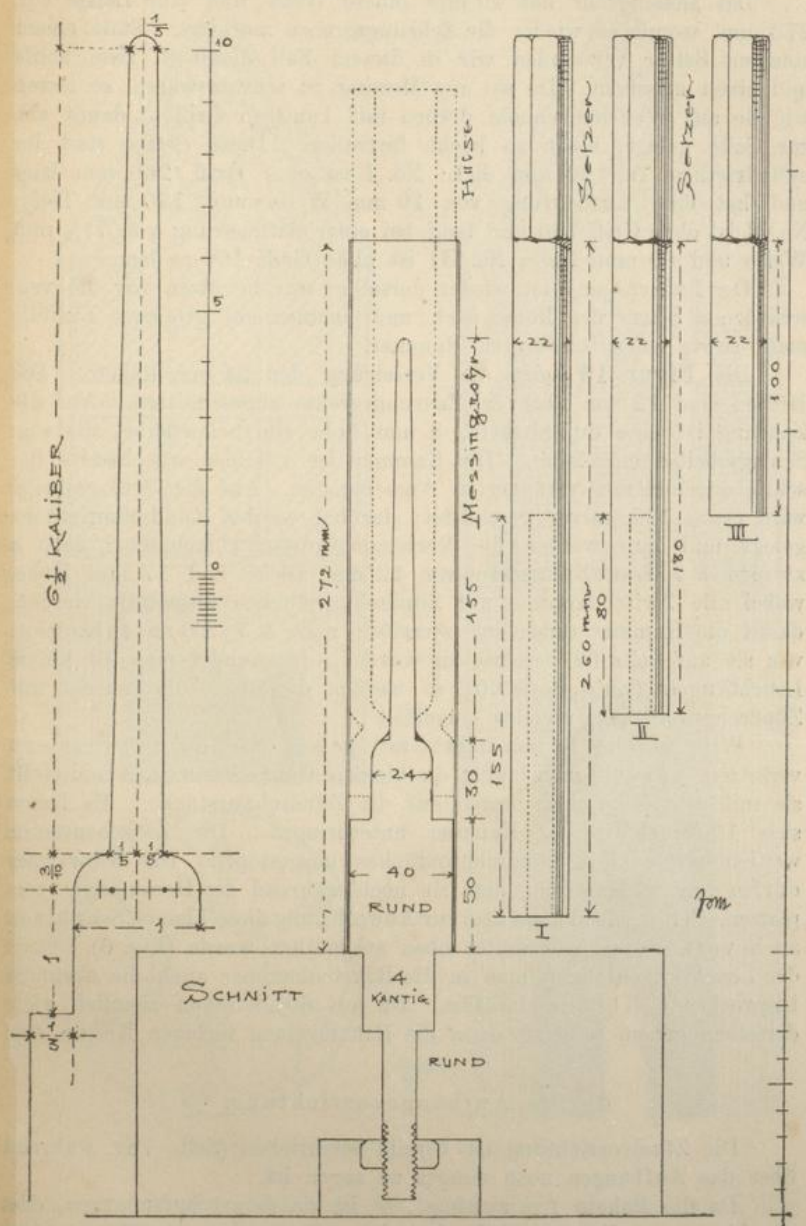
Untersatz und Setzer für die 24 mm-Rakete.
